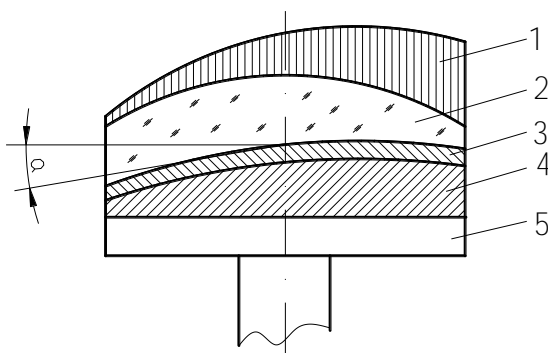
Схема блокировки заготовки при обработке призматической линзы:
